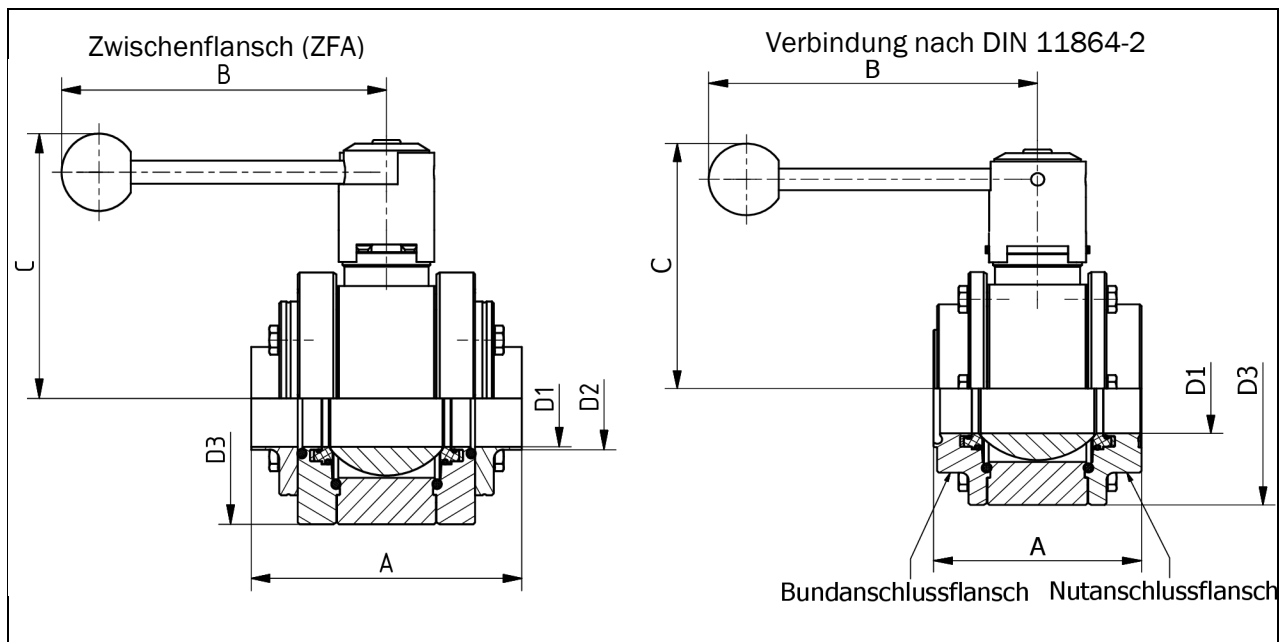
Kugelventil mit Handgriff: Anschlussvariante ZFA, DIN 11864-2
